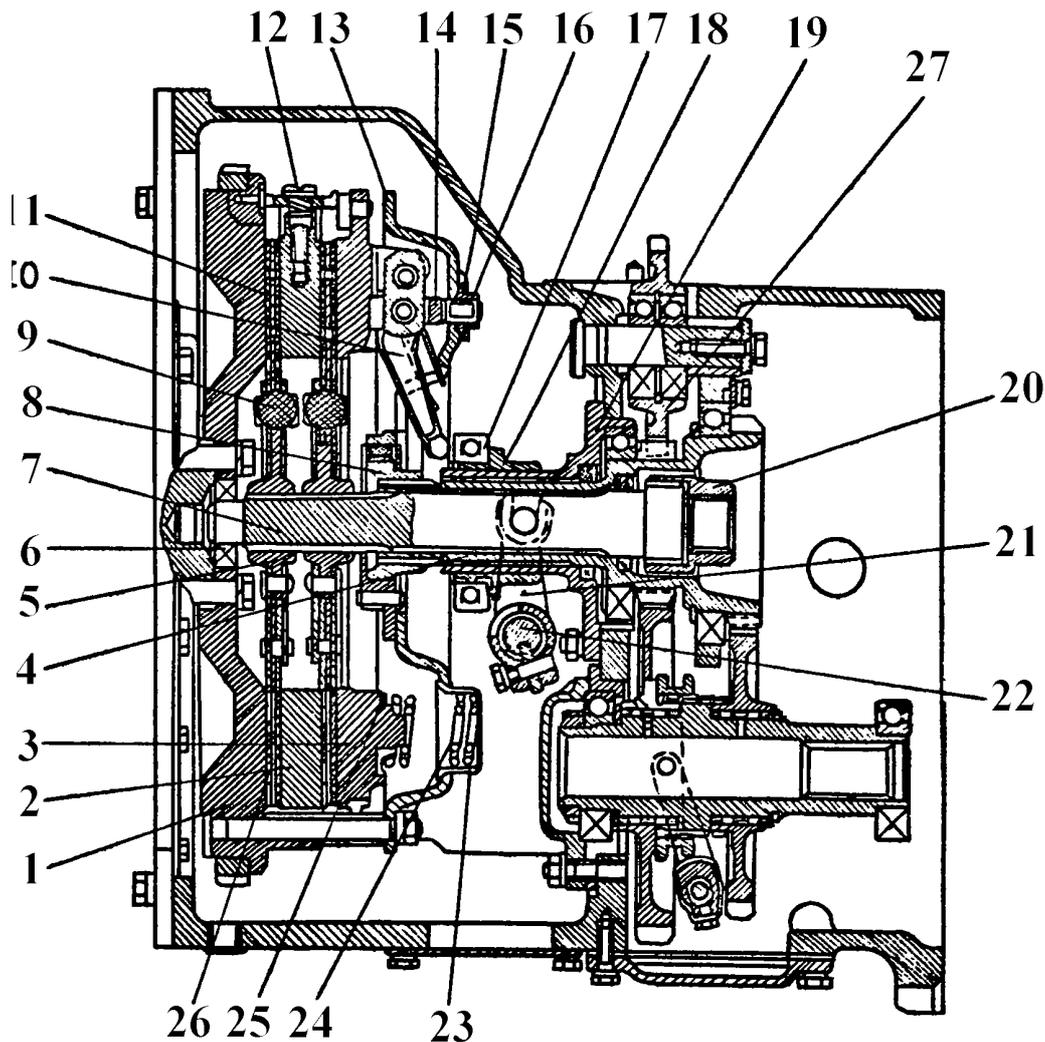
Сцепление: 1 - маховик; 2 - диск средний; 3 - диск нажимной; 4 - вал ведущий; 5 - ступица; 6 - подшипник; 7 - вал силовой; 8 - ступица; 9 - гаситель крутильных колебаний; 10 - рычаг отжимной; 11 - накладка фрикционная; 12 - рычажный механизм; 13 - опорный диск; 14 - вилка; 15 - шайба; 16 - гайка регулировочная; 17 - подшипник выжимной; 18 - отводка; 19 - кронштейн; 20 - втулка соединительная; 21 - вилка; 22 - валик управления; 23 - стакан; 24 - пружины; 25 - прокладка теплоизолирующая; 26 - диск ведомый; 27 - шестерня промежуточная
